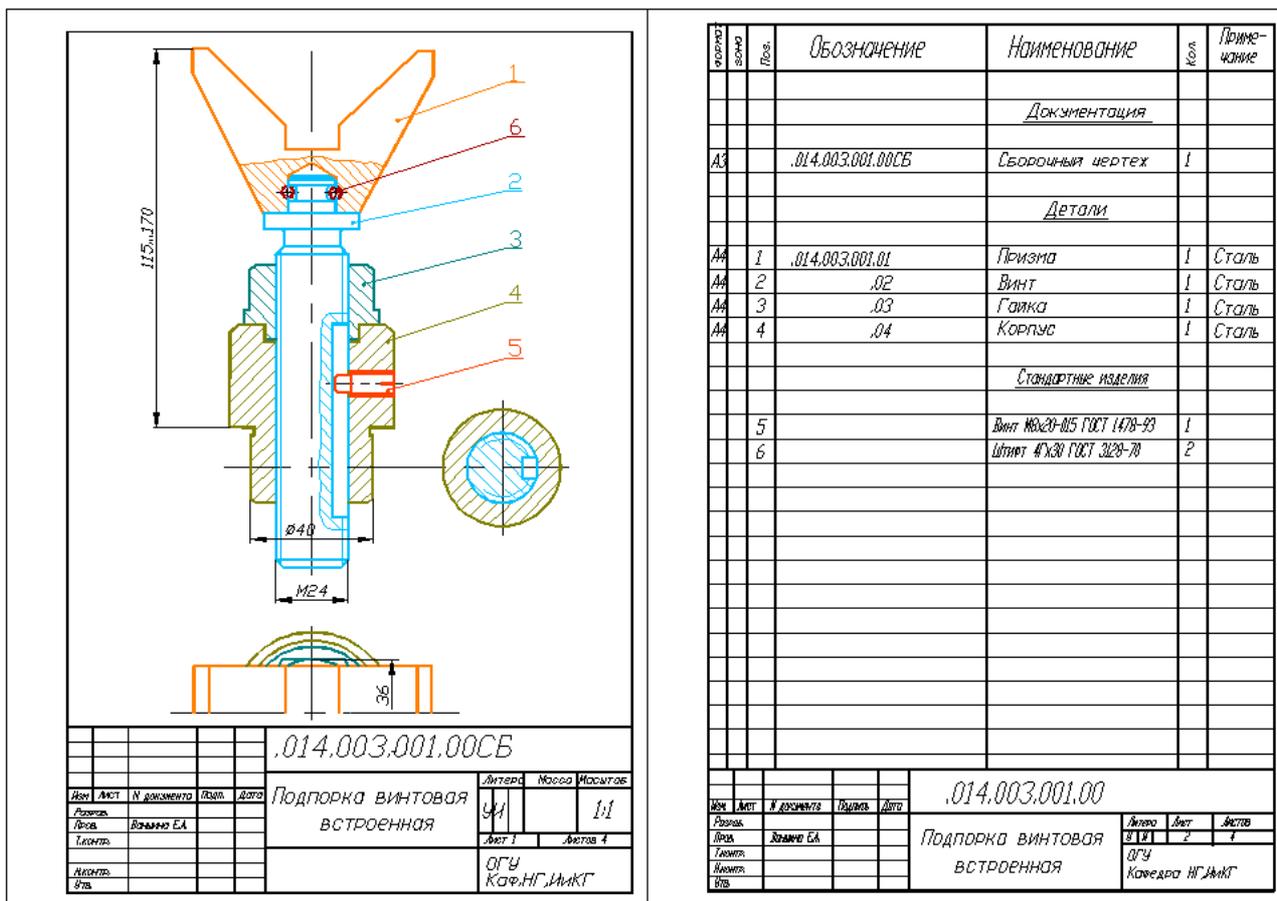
Сборочный чертеж «Подпорка винтовая встроенная».
